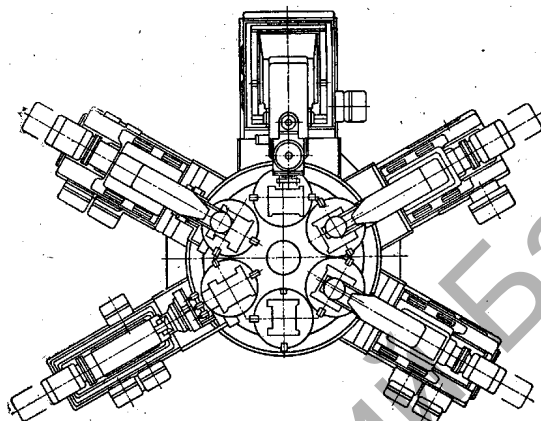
Многопозиционный агрегатный станок с поворотным столом
